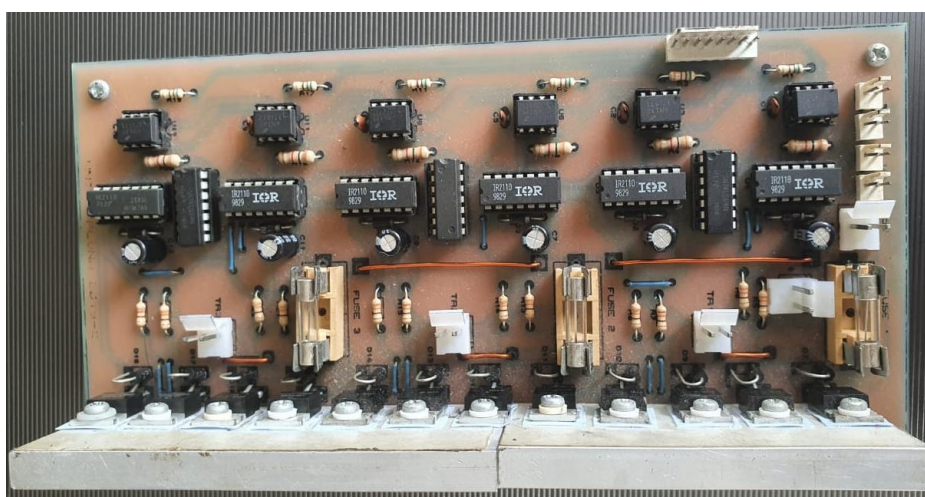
PCB inversor multinivel 3 etapas monofásico ensamblada
